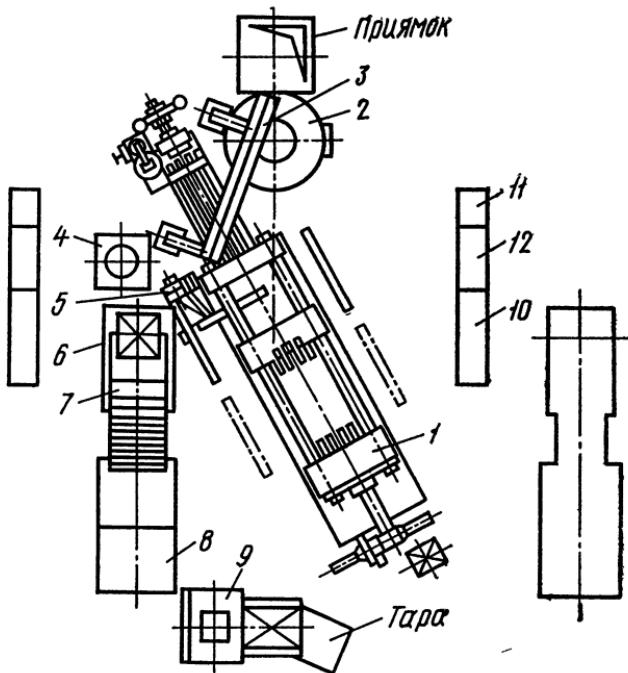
Схема расположения оборудования автоматизированного комплекса литья под давлением:
